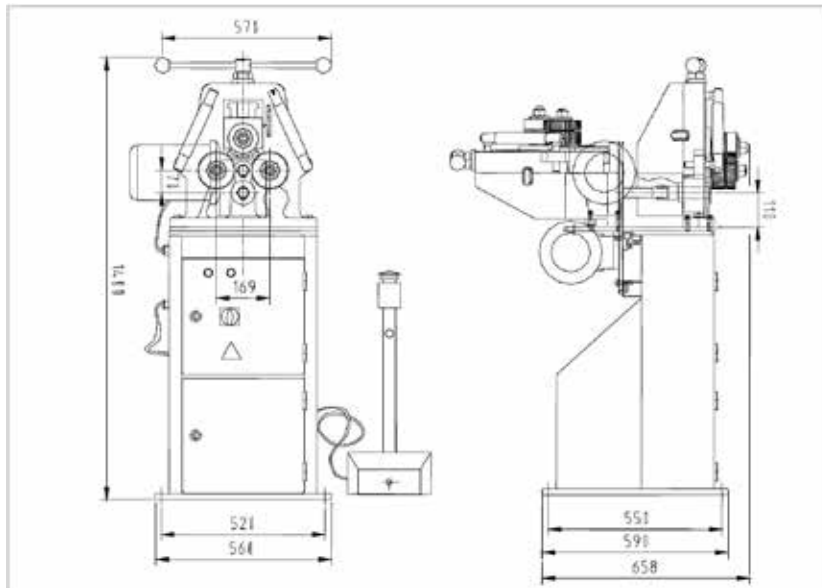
Dimensions pour l'installation de la cintruse PRM10 E
